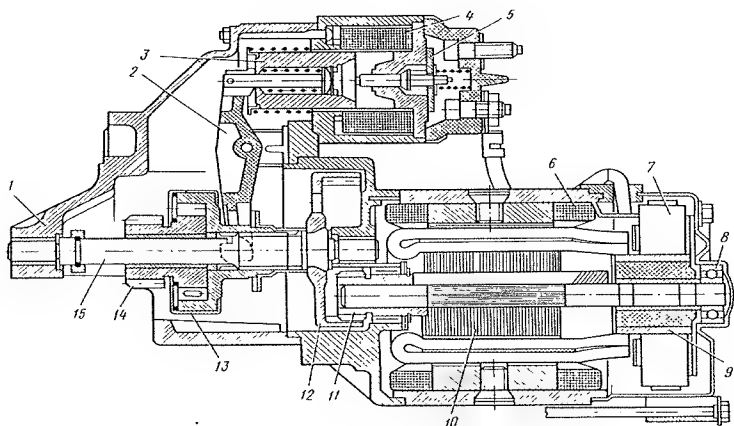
Стартер с редуктором и внутренним зацеплением [8]:
